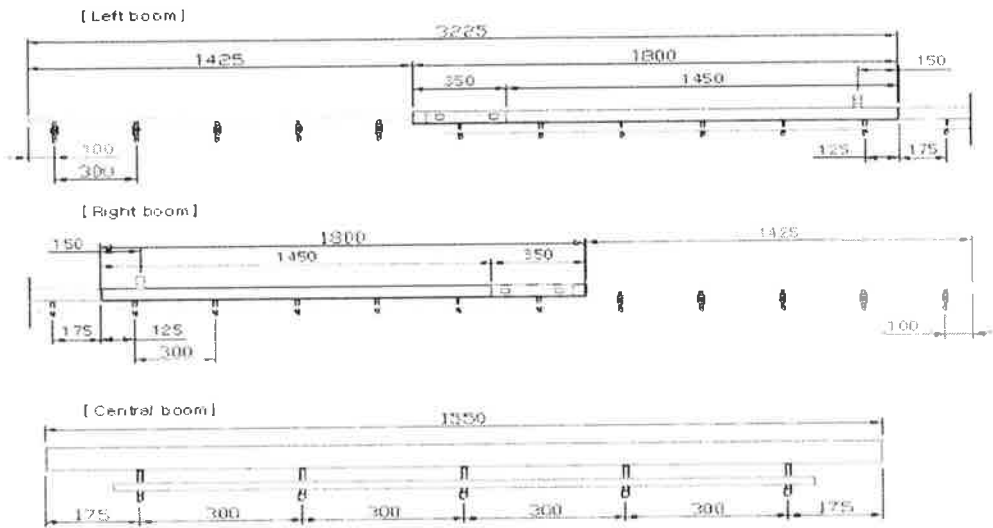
Nozzle arrangement of broadcasting boom(Dimension in cm).
